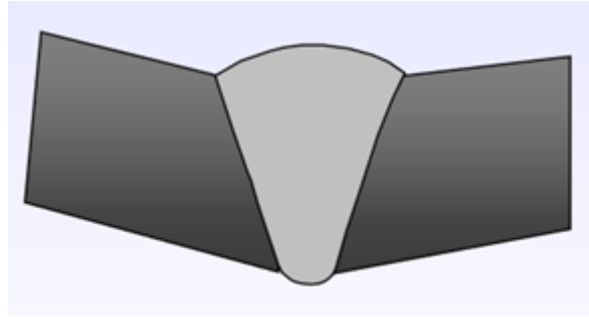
Nealiniere unghiulară. Sursă: M.S. Rogers, Welding Inspection Defects/Repairs Course Reference WIS 5, 2003.
